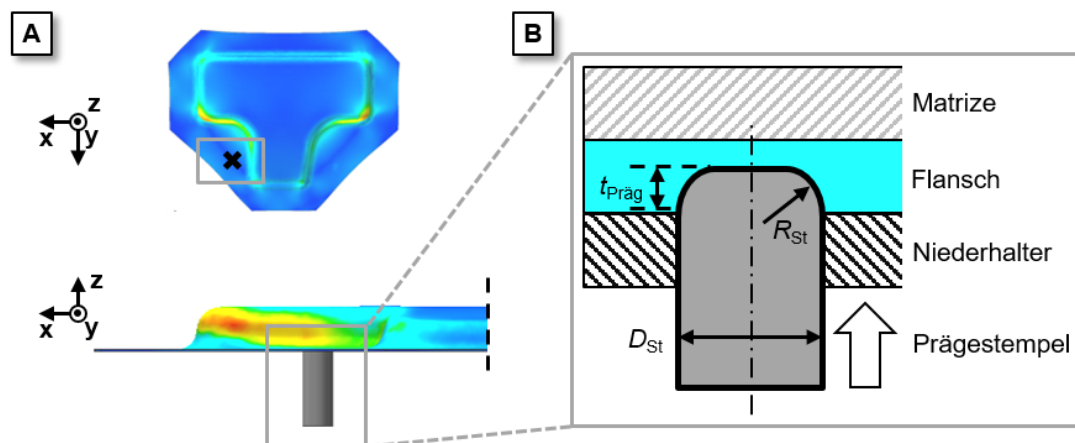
(A) Position der Prägestempel im Flansch des Demonstrators und (B) Geometrie des Stempels für die Prägungen
